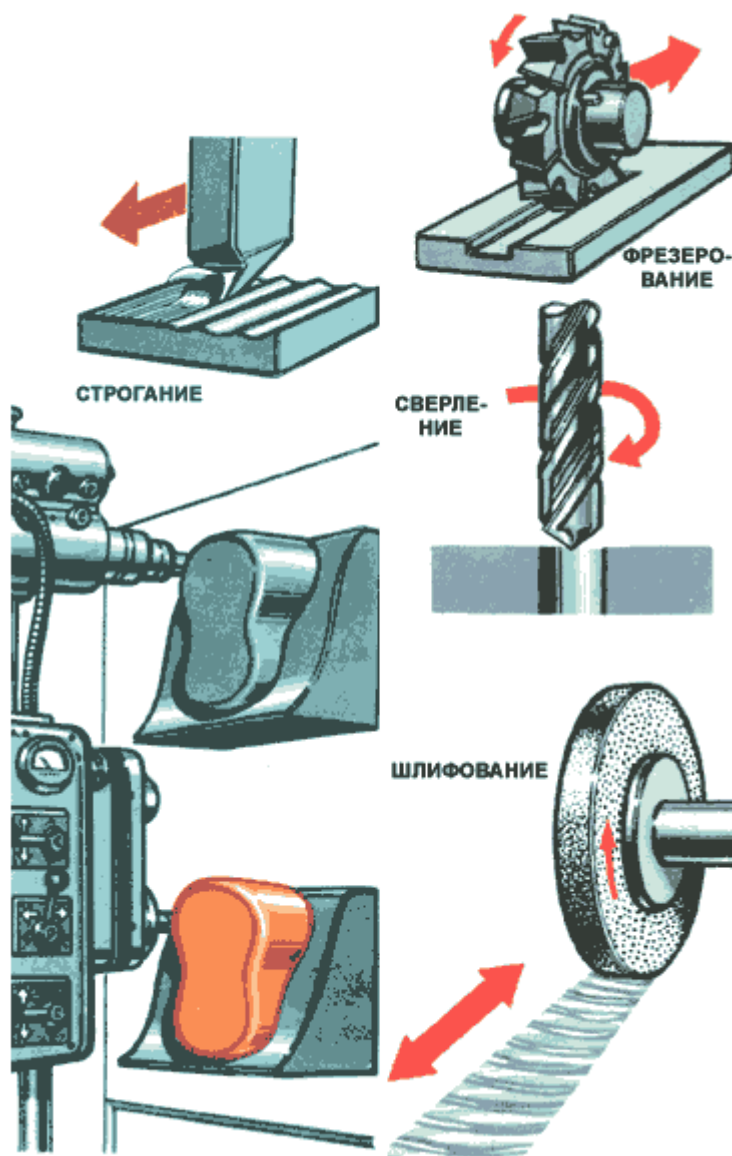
Примеры механообработки: строгание, фрезерование, сверление, шлифование.
